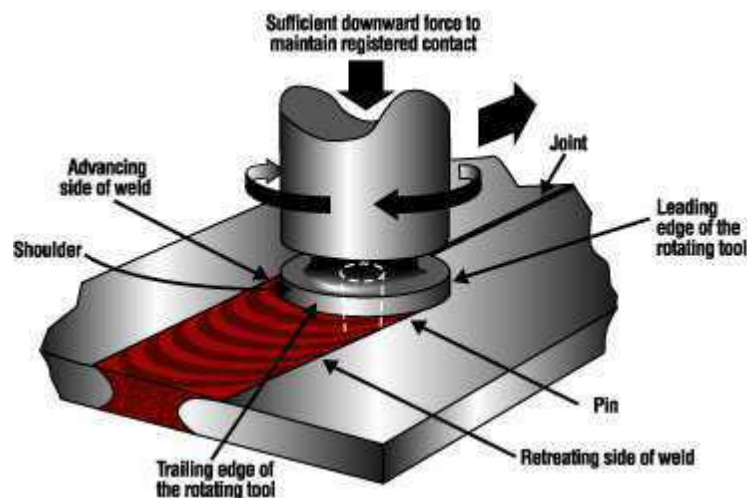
Proses *Linear Stir Welding
